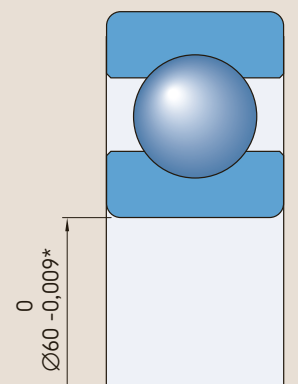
Подшипник качения с размером и допуском на диаметр отверстия.
